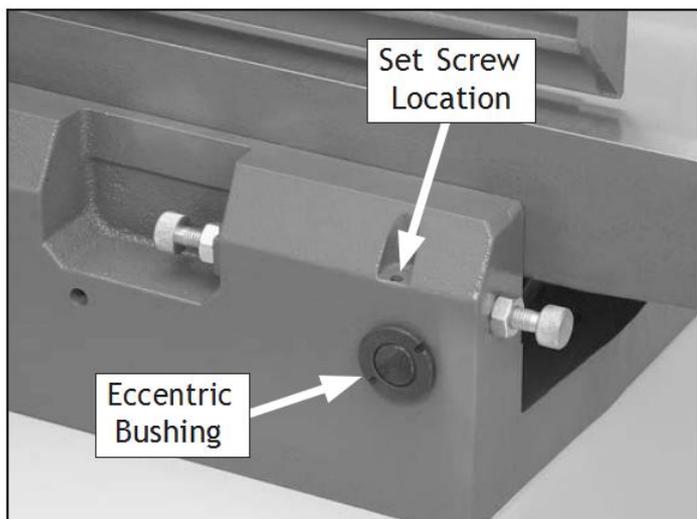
Расположение эксцентриковой втулки и установочного винта.
